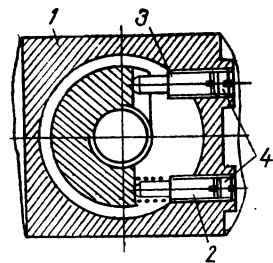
Разрез читающей системы: 1 — корпус; 2, 3 — регулировочные винты; 4 — заглушки
